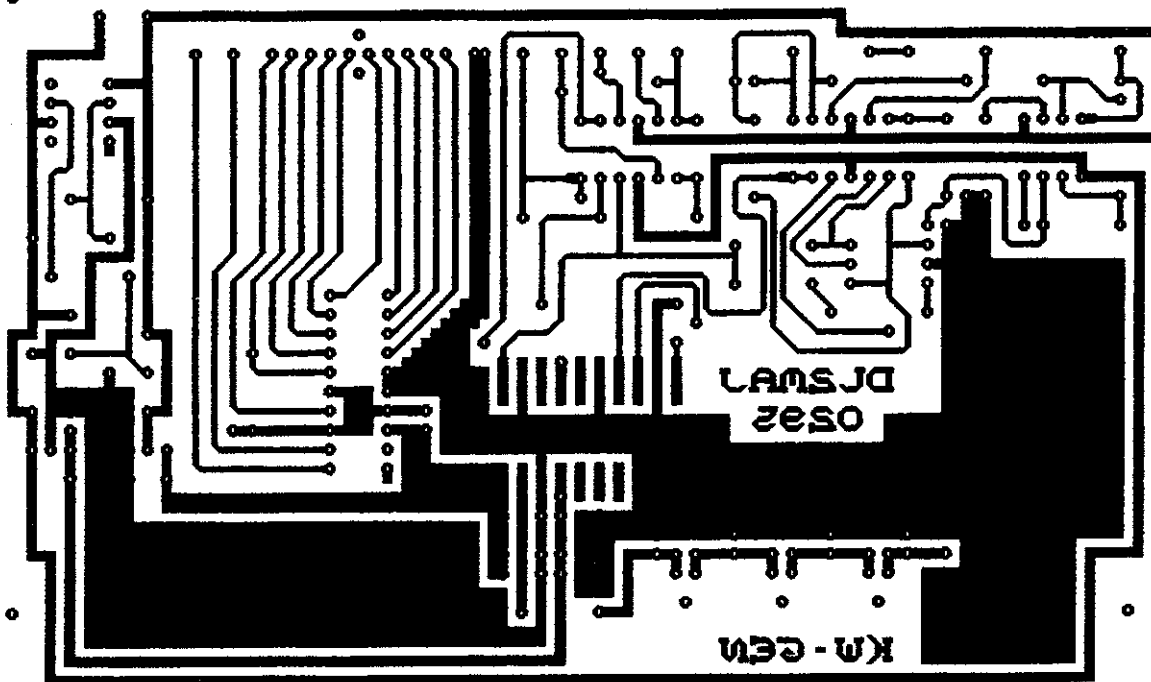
Printlayout. MAX038 monteres oven på printet.
